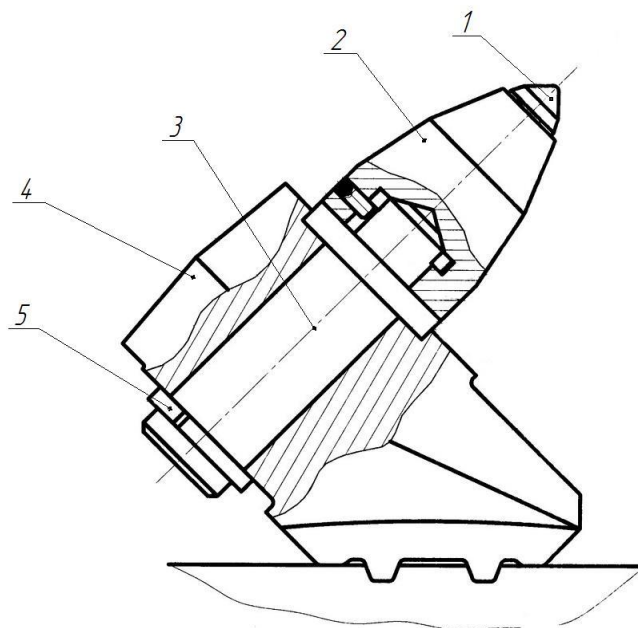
Составной резец авторов [47]: 1 – твердосплавная вставка; 2 – съемная головка державки; 3 – хвостовик; 4 – резцедержатель; 5 – фиксатор.
